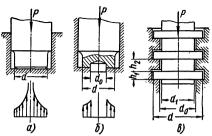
Упорные подшипники: а — со сплошной пятой; б — с кольцевой опорной поверхностью; в — гребенчатый
